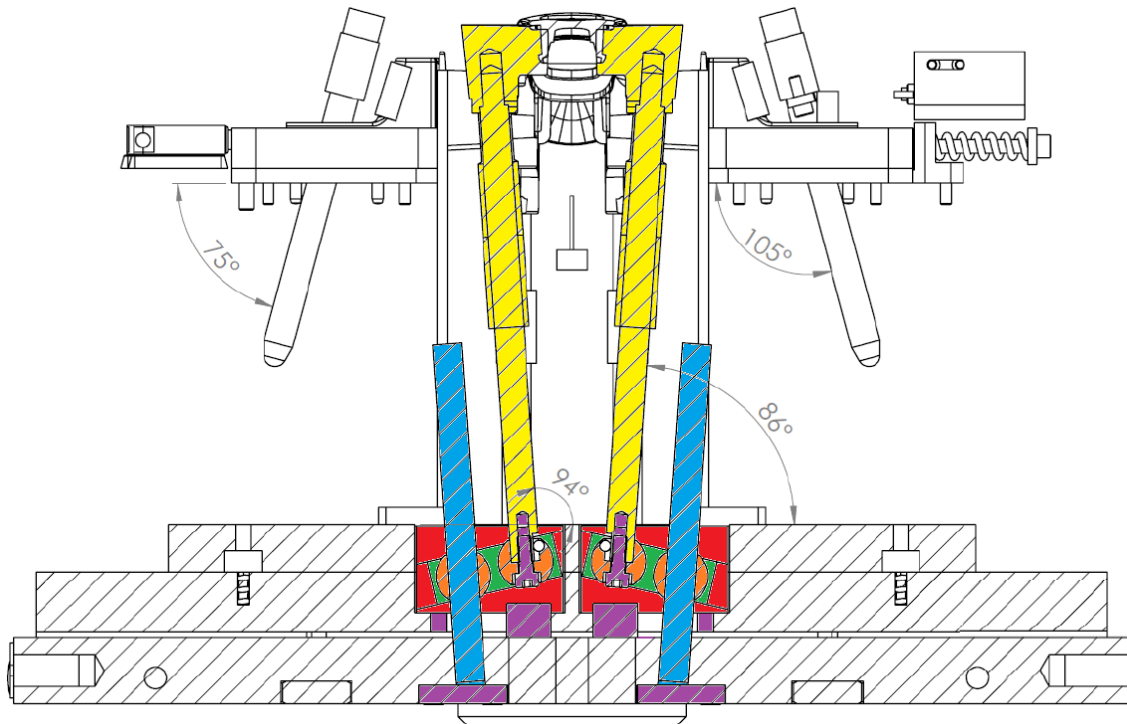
Desenho técnico da vista em corte dos levantadores de 4°
